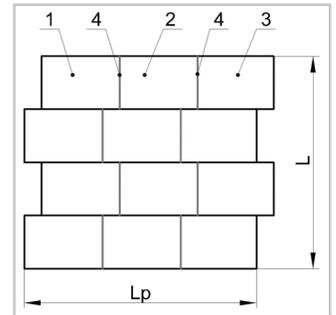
Схема условной развертки обечайки, свариваемой из царг: 1, 2 и 3 – листы составной развертки царги; 4 – продольный сварной шов царги; L_p – длина развертки царги; L – длина обечайки
